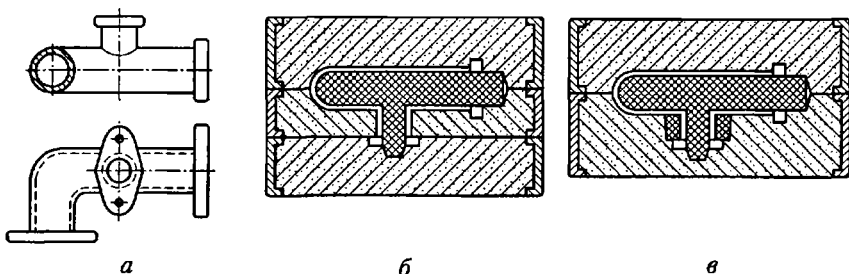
Эскиз сложной отливки и опоки ручной и машинной формовки:
